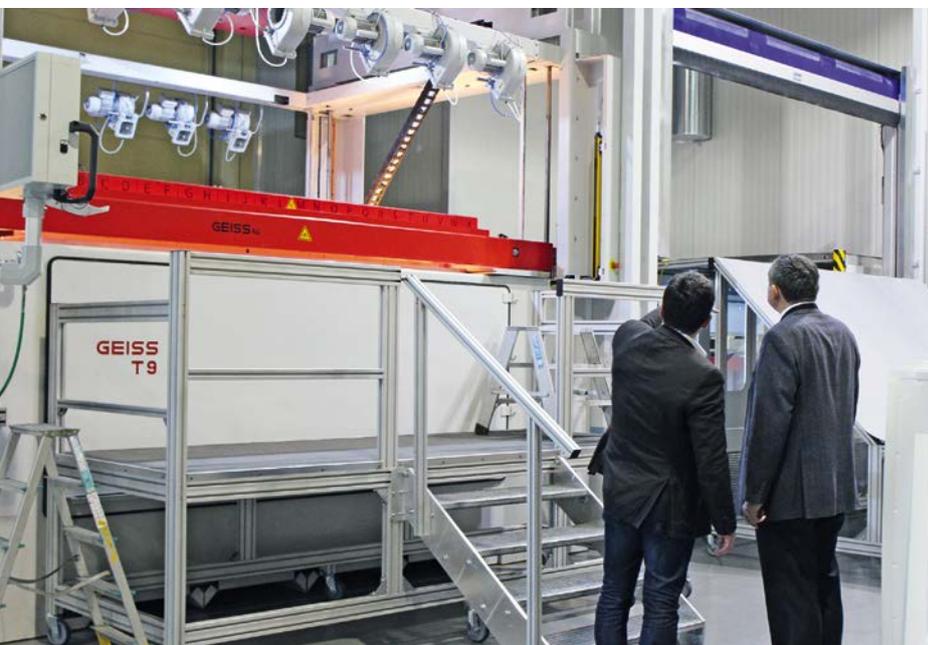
Thermoformmaschine für sehr große und komplexe Dimensionen (Bilder: Parat)
